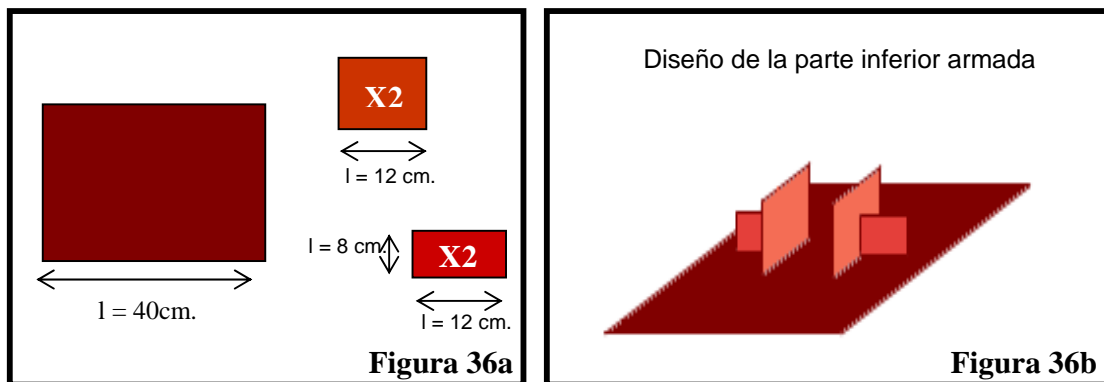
EL panel a) muestra las dimensiones de cada una de las cinco piezas. El panel B)muestra la imagen de la parte inferior ensamblada.
